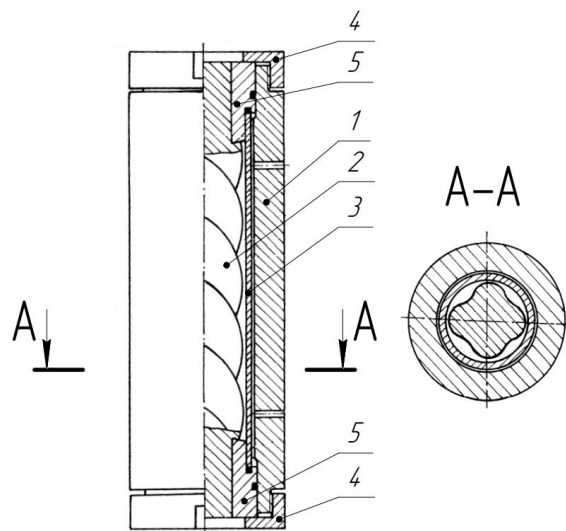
Общий вид формы для гидроформовки корпуса обоймы одновинтового насоса:
